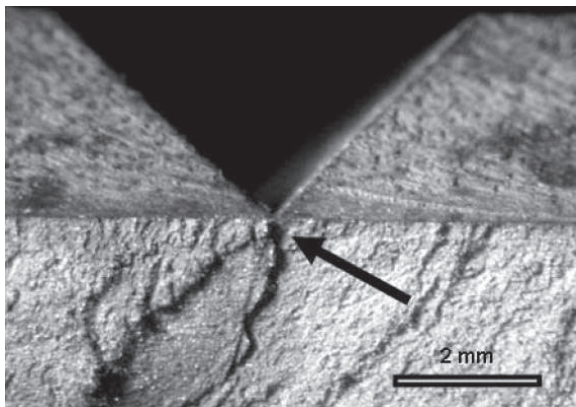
Superficie de fractura de la mordaza. Sitio de inicio de grieta entre dos dientes adyacentes
